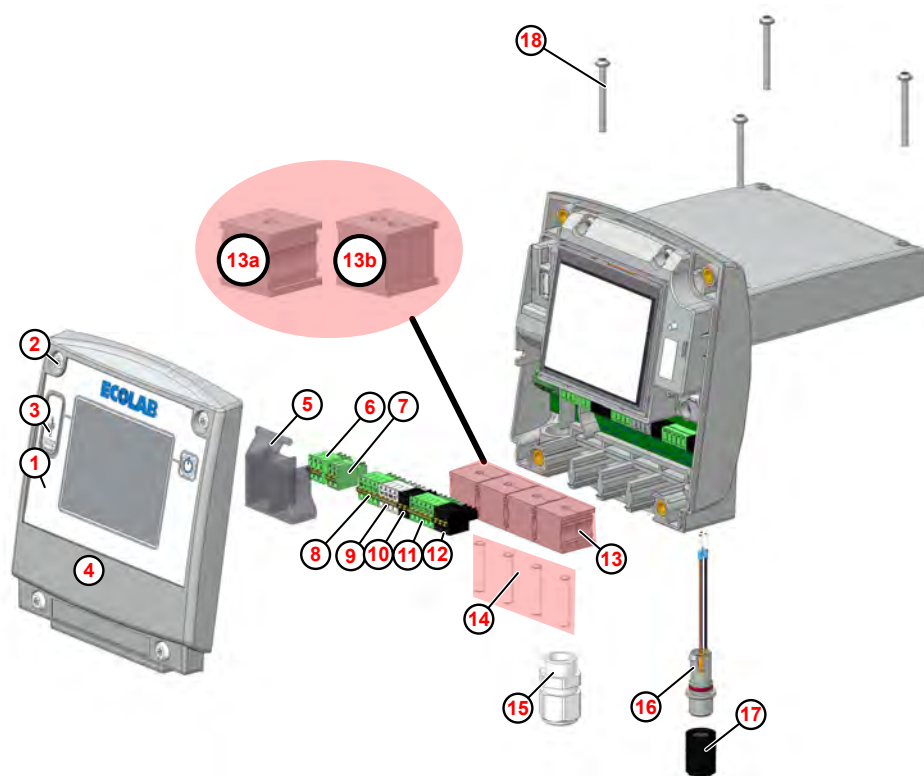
Couvercle d'écran - unité de commande « EcoAdd »
